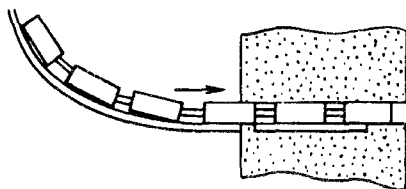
Схема обработки заготовки на бесцентрово-шлифовальном станке
